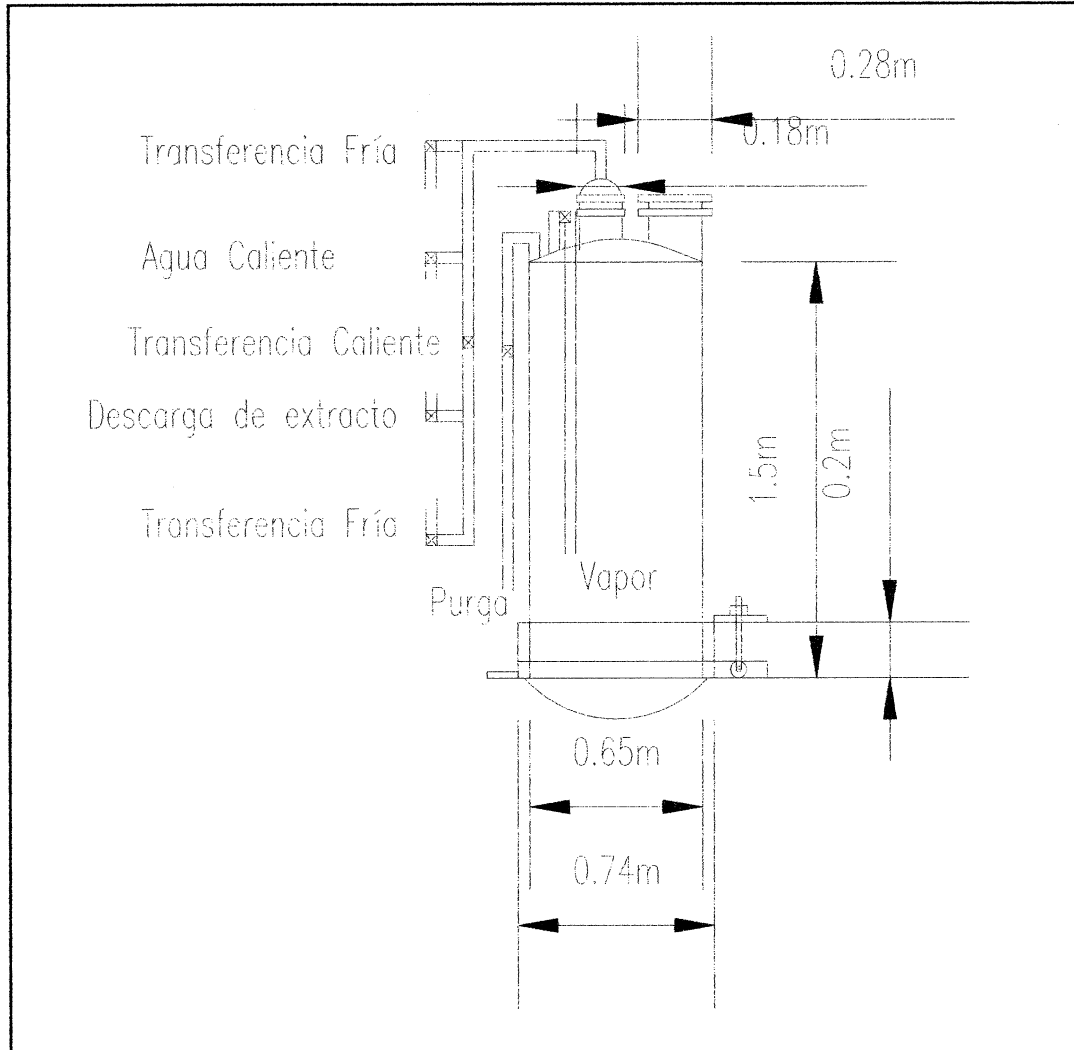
Dibujo del banco de extracción de la planta piloto vista lateral
